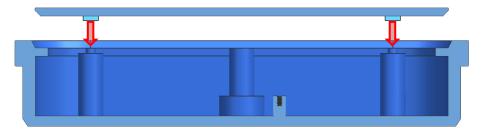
Corte lateral da tampa com destaque para os encaixes da tampa
